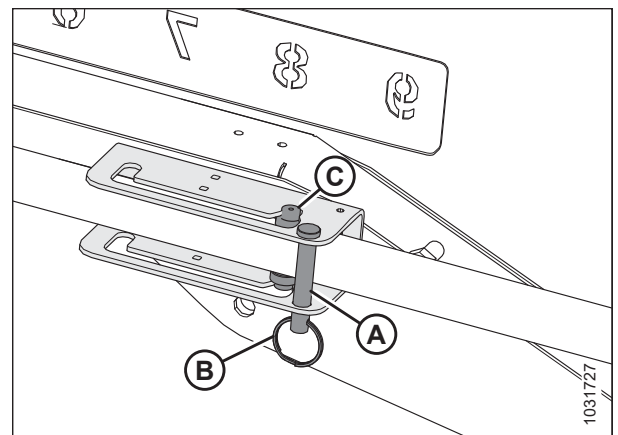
Justering af frem/tilbage-cylindere type 2 – frem-position
